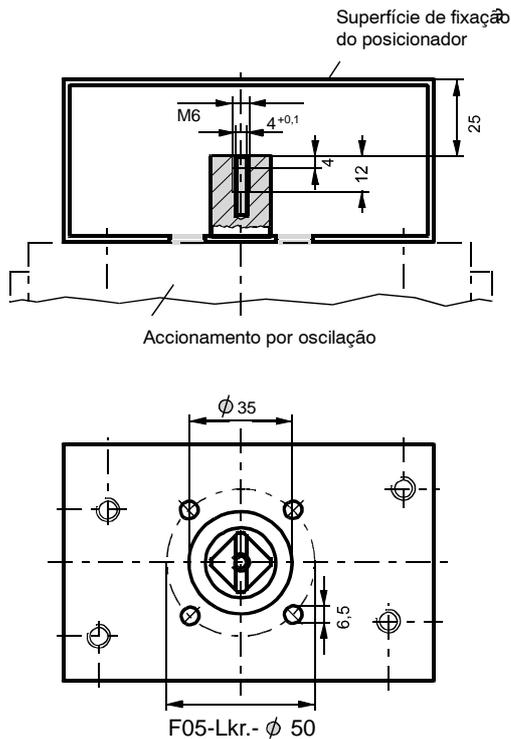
Montagem dos accionamentos giratórios, consola de montagem (âmbito de fornecimento do fabricante de accionamento), dimensões
